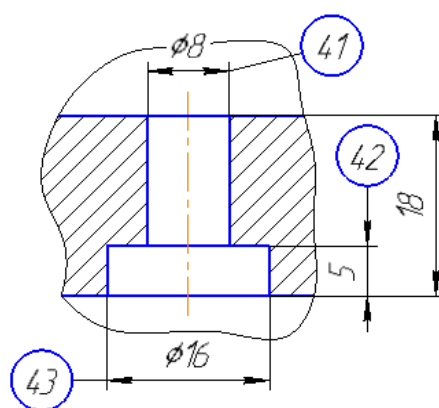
Эскиз детали «Корпус гидроцилиндра шибера затвора»
